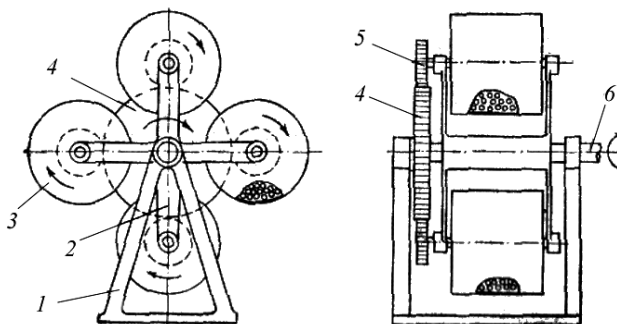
Планетарний млин: 1 – станина; 2 – водило; 3 – барабанний млин; 4 – нерухоме зубчасте колесо; 5 – приводна шестірня; 6 – приводний вал
